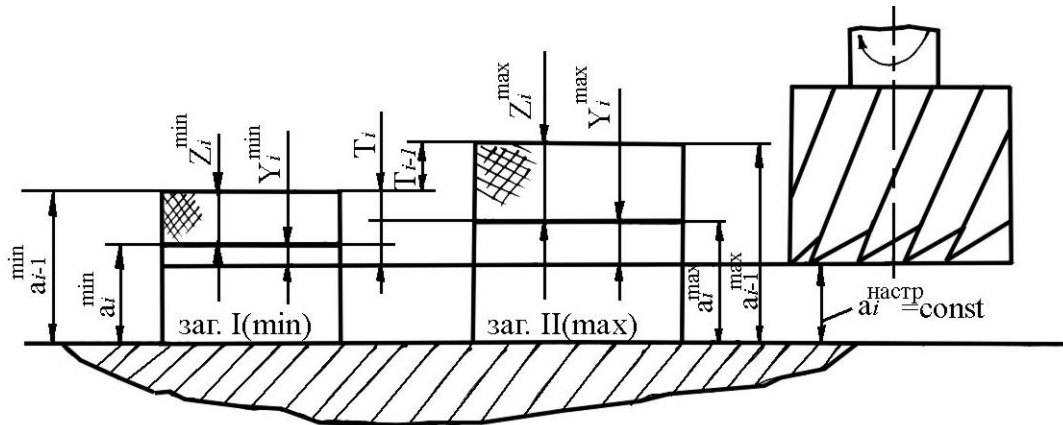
Схема фрезерування заготовок на налагодженому верстаті
